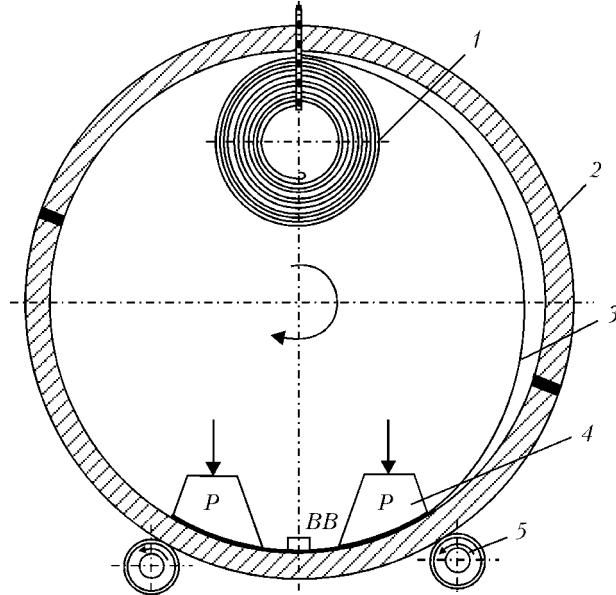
Принципиальная схема плакирования внутренней поверхности цилиндрических сосудов с использованием сварки взрывом: 1 — рулон, свернутый из полотна плакирующего металла; 2 — корпус сосуда; 3 — полотно плакирующего металла; 4 — прижимы; 5 — роликовый стенд
